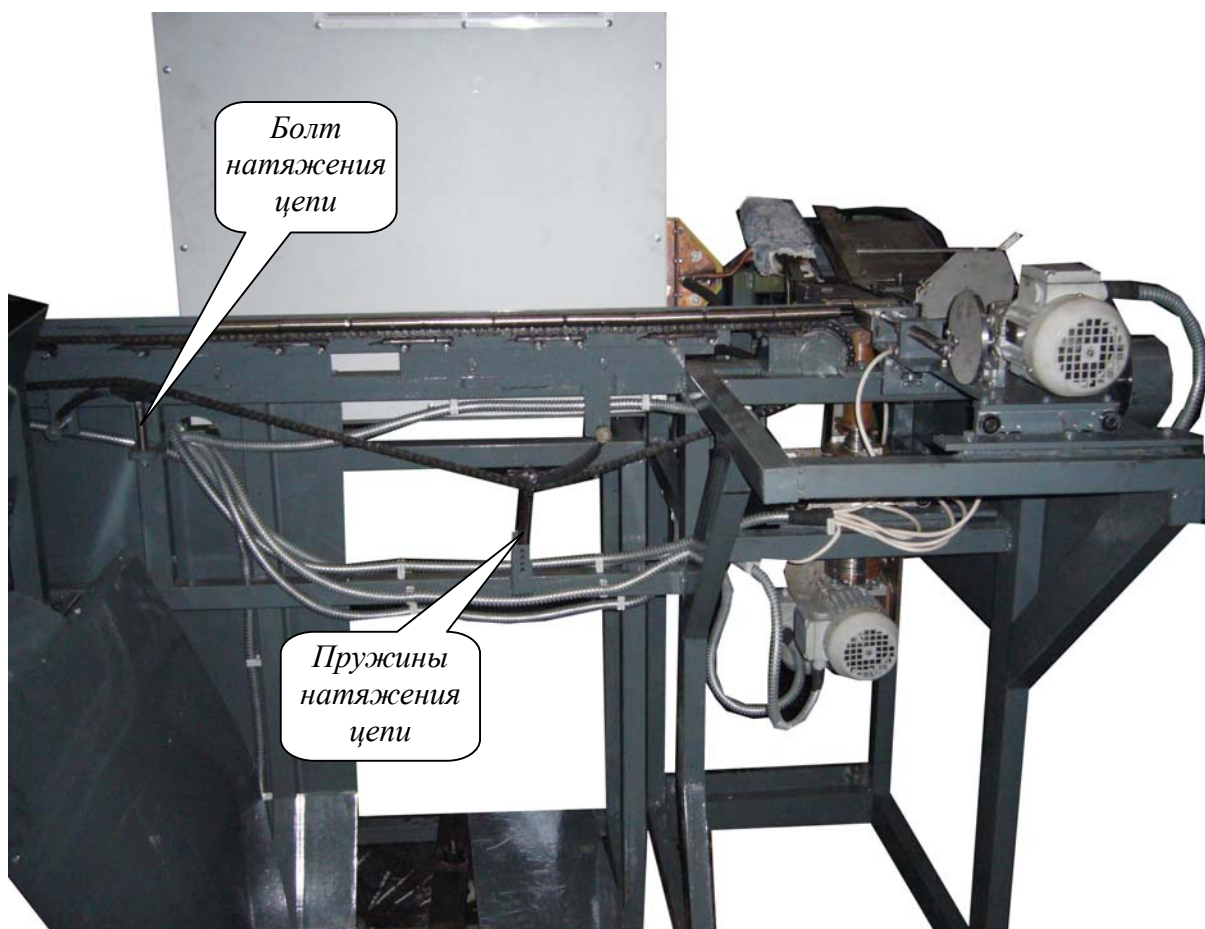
Общий вид цепного механизма подачи заготовок
